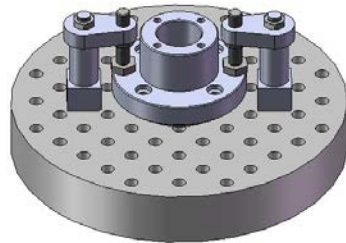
Компонування верстатного пристрою для обробки фланця
